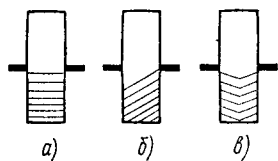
Условные обозначения зубчатых колес с прямыми (*а*), косыми (*б*) и шевронными (*в*) зубьями
